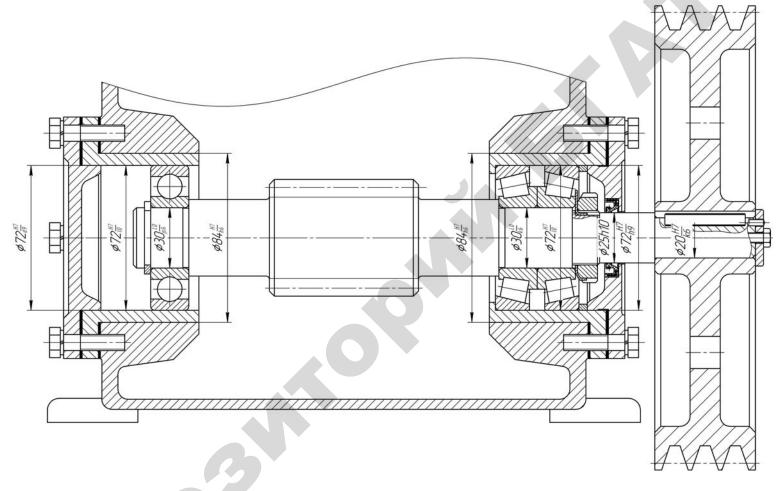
Фрагмент сборочного чертежа одноступенчатого червячного редуктора
